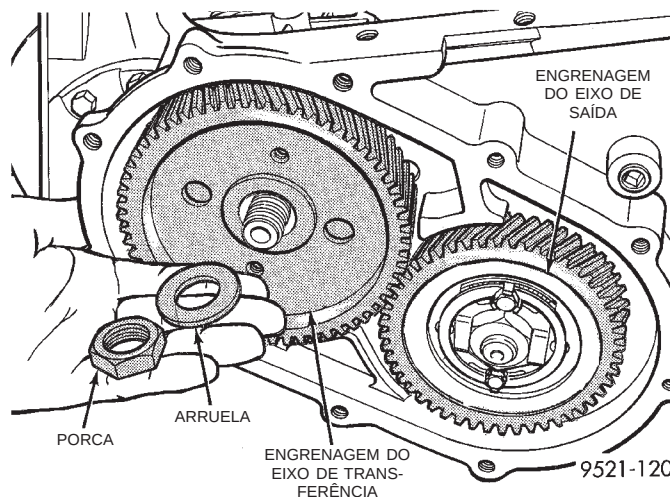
Porca e Arruela da Engrenagem do Eixo de Transferência
